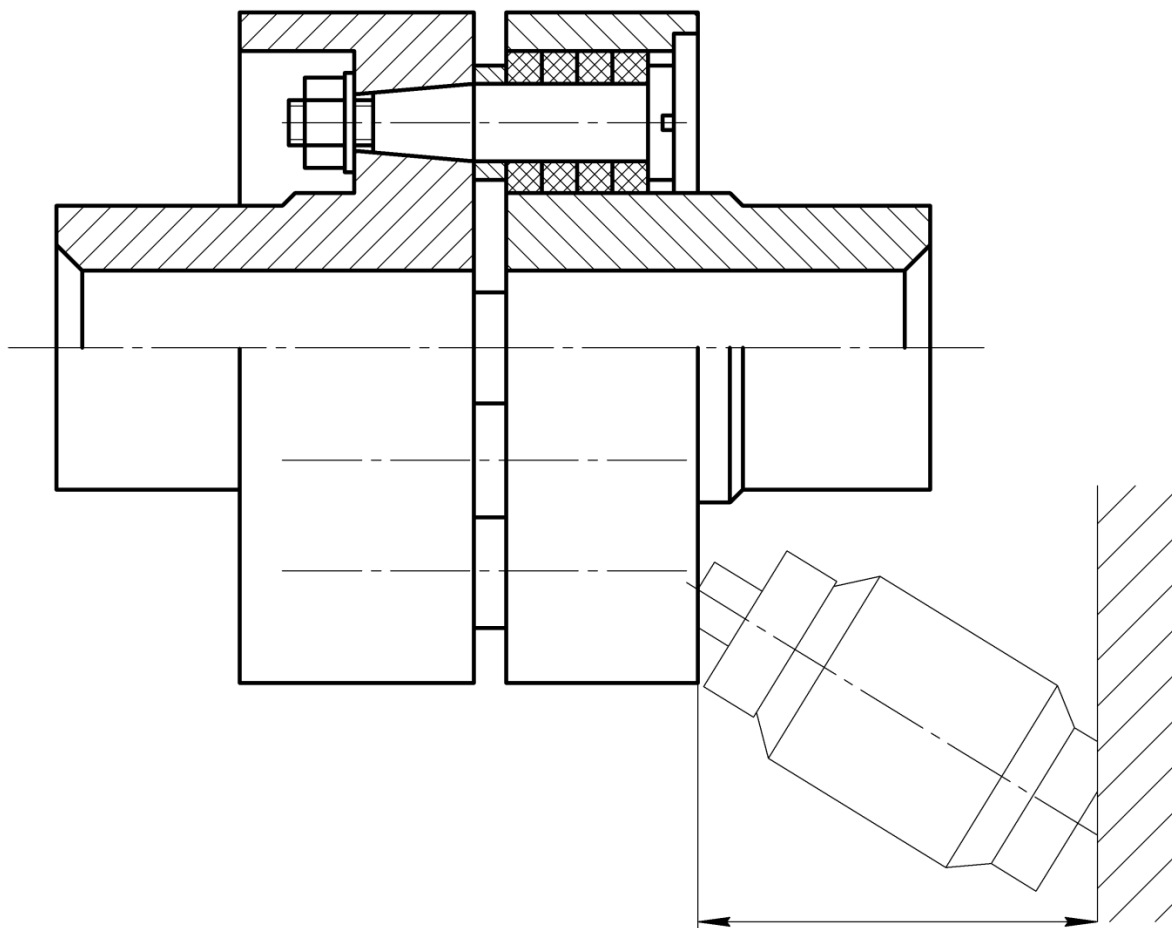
Сборочный чертеж муфты с «обстановкой»
